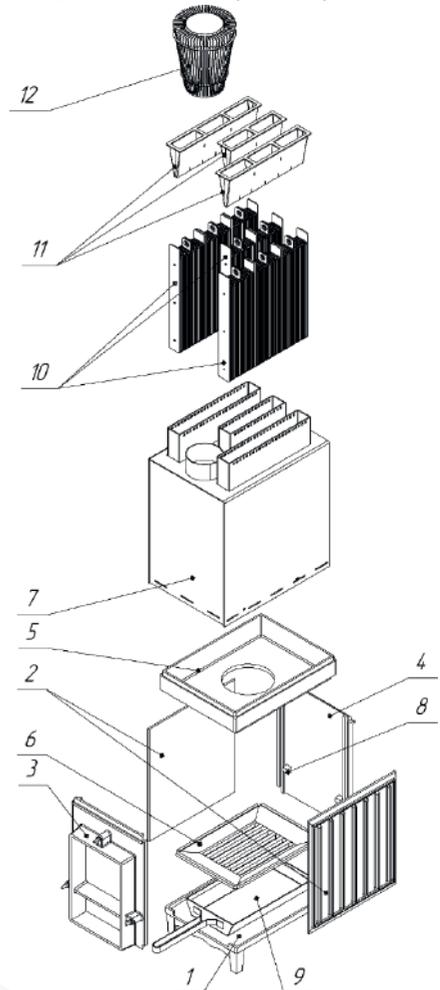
Схема сборки топочного агрегата печи Сударушка Чистопар.
